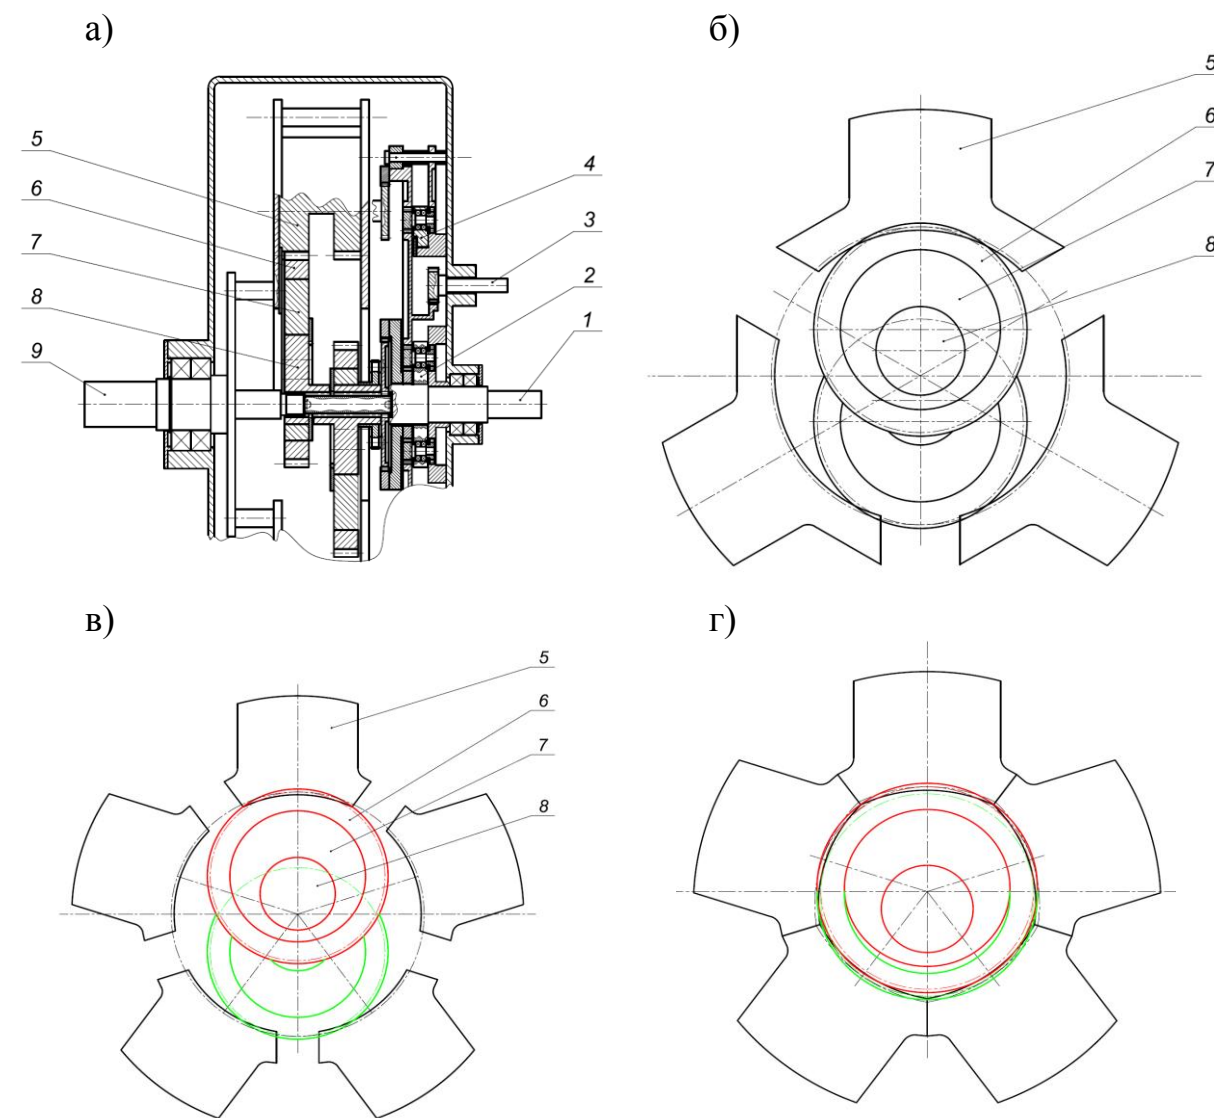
Компонировка планетарной плавнорегулируемой передачи по схеме 2: а – принцип действия передачи; б – схема расположения секторов центрального зубчатого колеса; в – пятисекторное центральное зубчатое колесо при минимальном передаточном отношении передачи; г – пятисекторное центральное зубчатое колесо при максимальном передаточном отношении передачи
